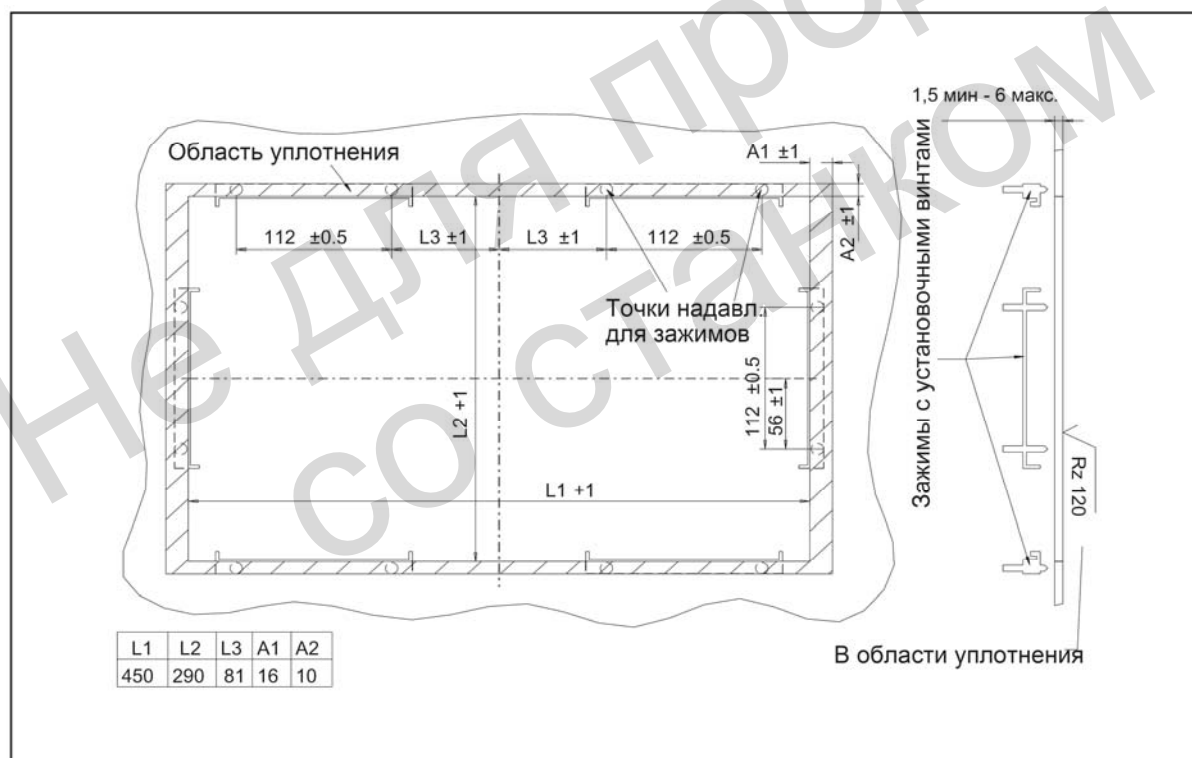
Габаритный чертеж для монтажа панели оператора ОР 015
